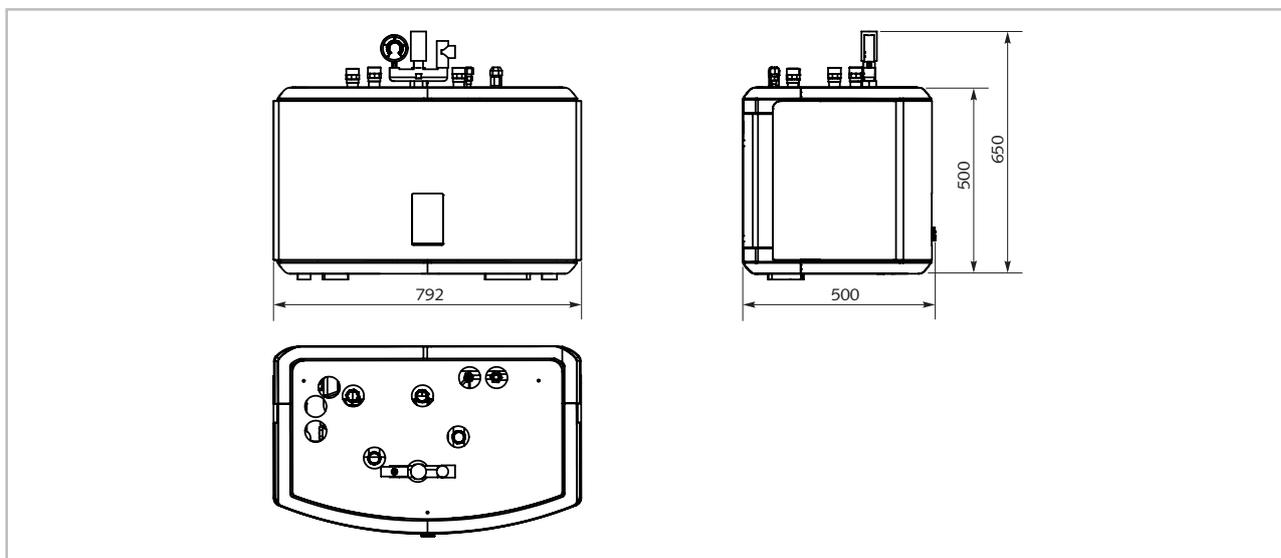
Dimensions du module intérieur de la série WKF 70/120/180 (Toutes les dimensions en mm)
